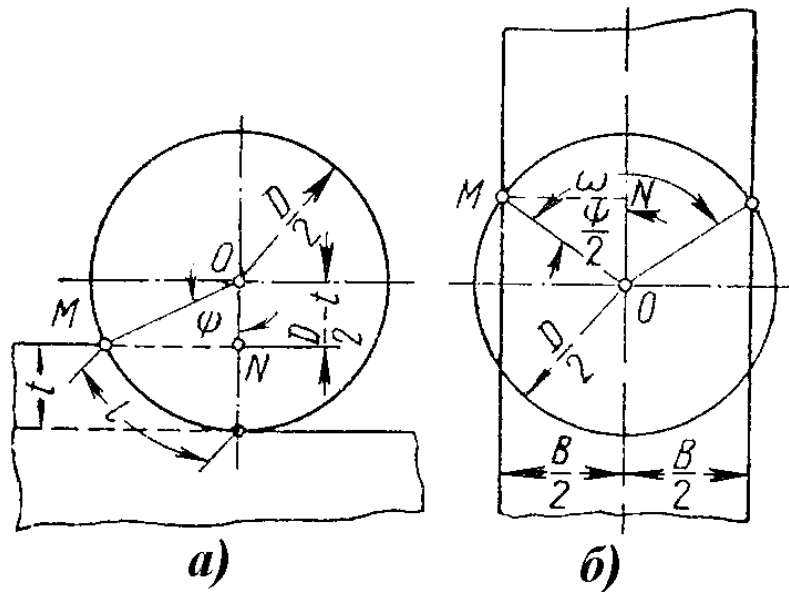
Угол контакта при фрезеровании: а – для цилиндрической фрезы; б – для торцовой.
